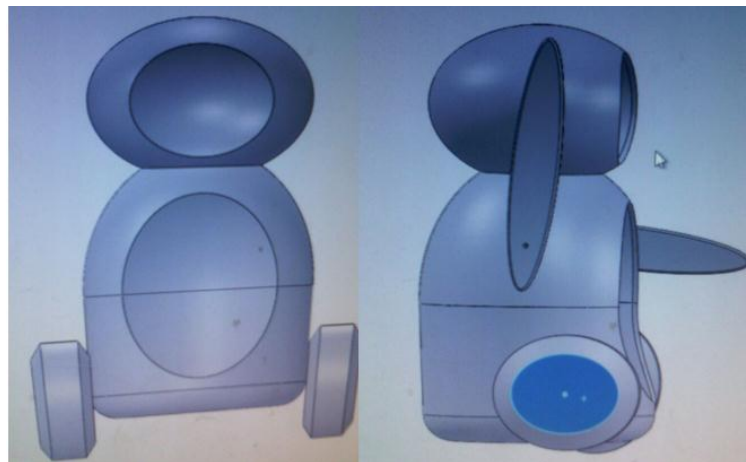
Estructura del Robot diseñada en SolidWorks.
